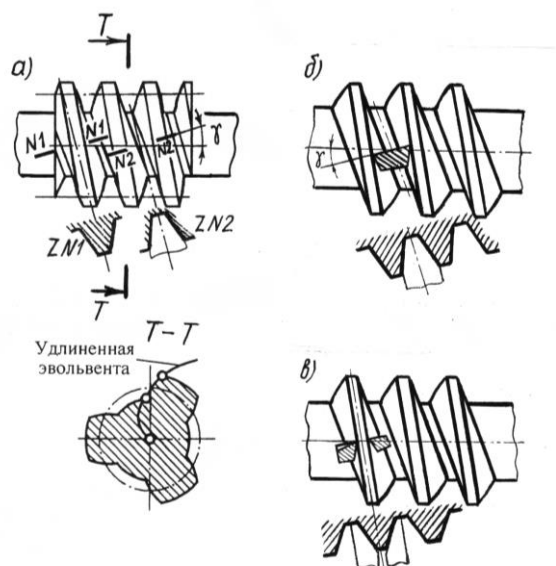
Конволютный червяк ZN (а) и схемы установки резцов с прямолинейным профилем: б – двустороннего резца для нарезания витка червяка ZN2; в – односторонних резцов для нарезания витка червяка ZN1
